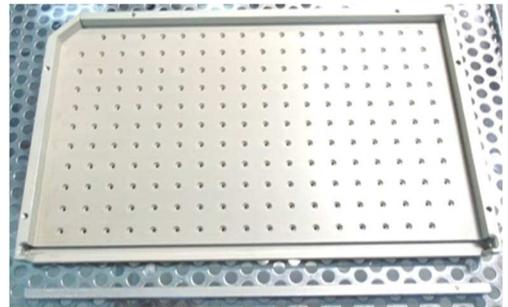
Production drawing JIG (Stick Frame bagian kanan)
